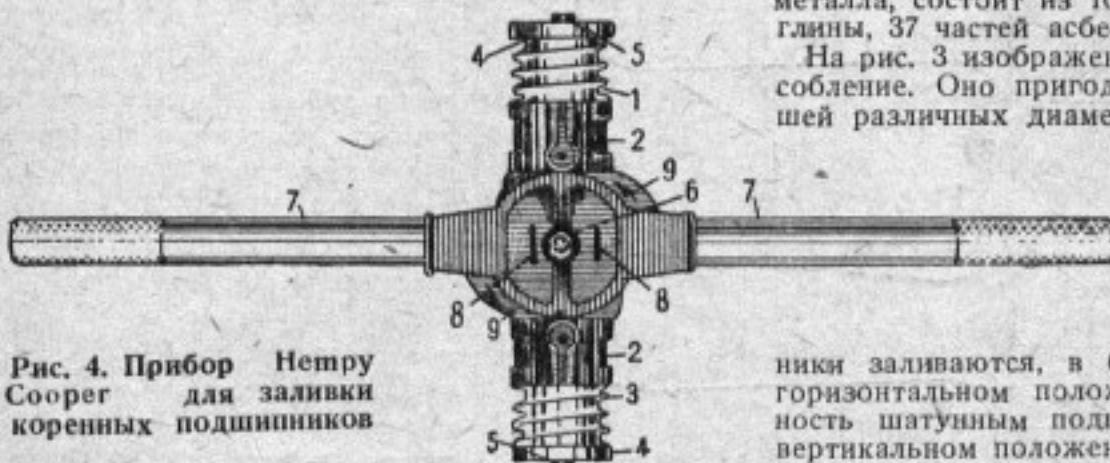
Прибор Немру Соорег для заливки коренных подшипников
